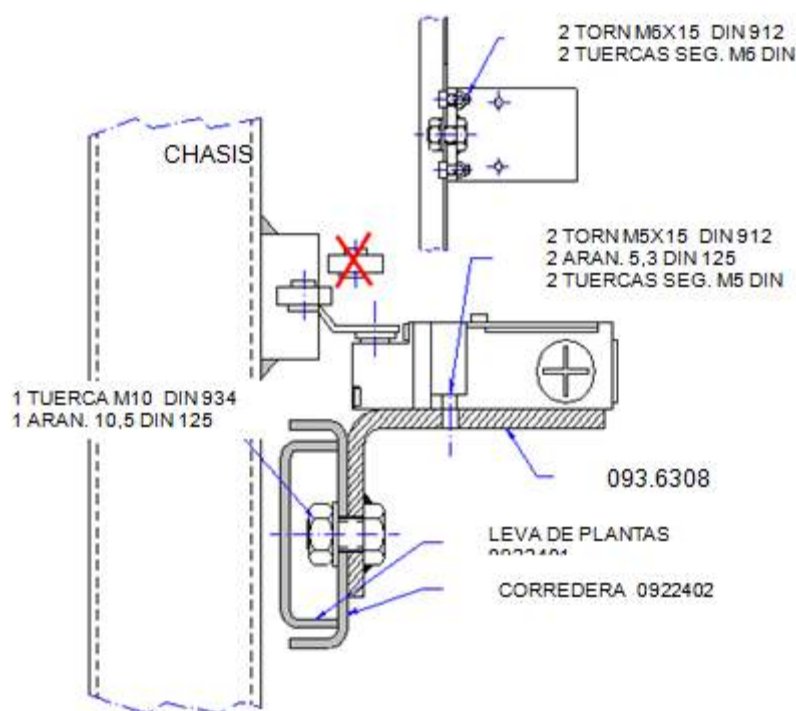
Colocación Micro Apertura Puerta Seg. Planta Altura Total
